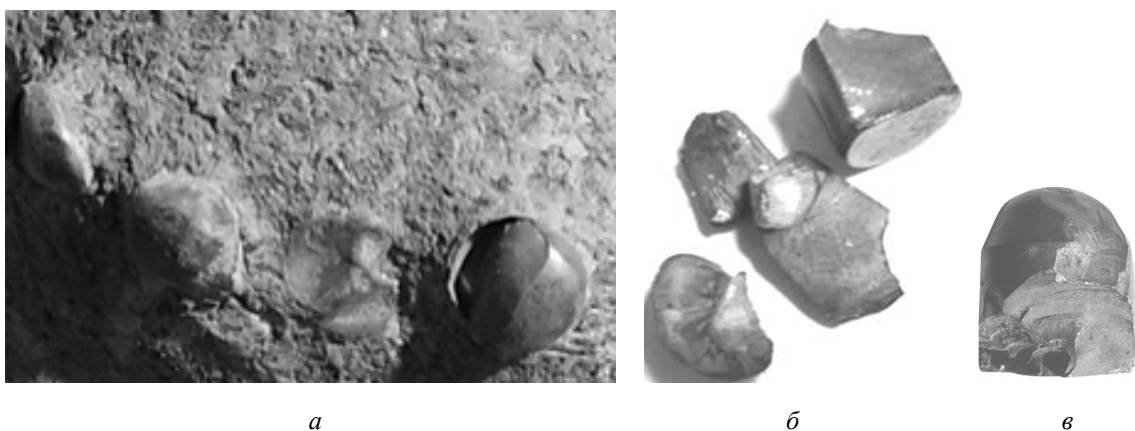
Види катастрофічного розколювання твердосплавних зубків: а – розколювання робочої поверхні твердосплавних зубків; б – фрагменти розколених вздовж осі твердосплавних зубків; в – розколювання у нижній ділянці хвостовика твердосплавного зубка
